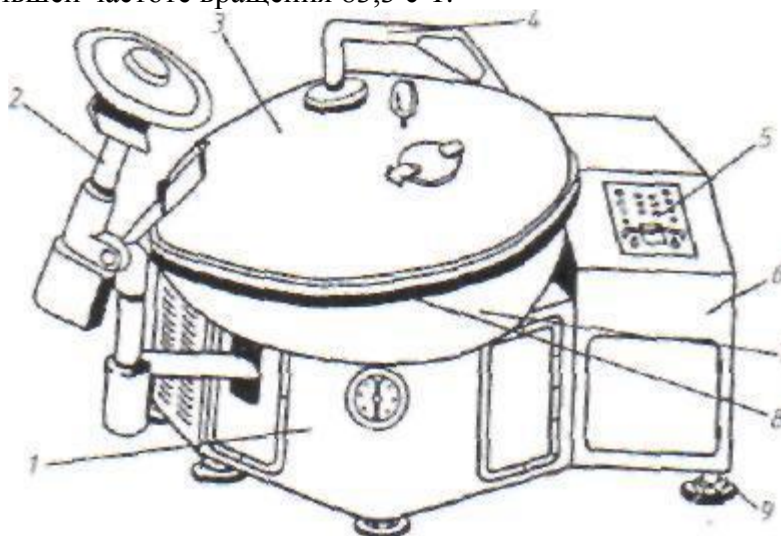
Вакуумный куттер ВК-125: 1 - корпус; 2 - механизм выгрузки; 3 - вакуумная крышка; 4 - рычаг; 5 - пульт управления; 6 - машинный отсек; 7 – вакуумный корпус; 8 - вакуумное уплотнение; 9 - виброопоры.
